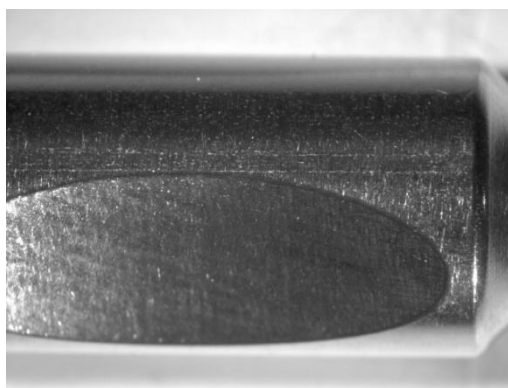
Bild efter fjärde vibrationstrumlingen.
